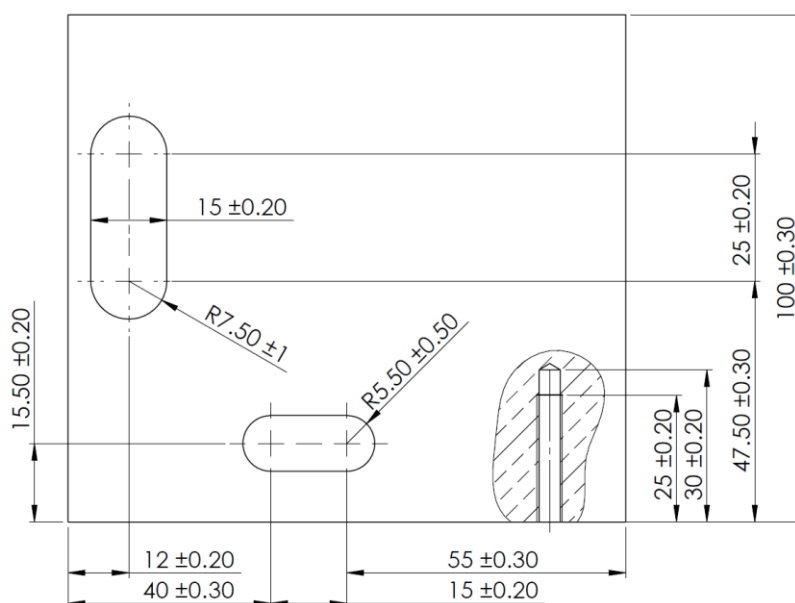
Toleranzen der Grundplatte des Haltewinkels
